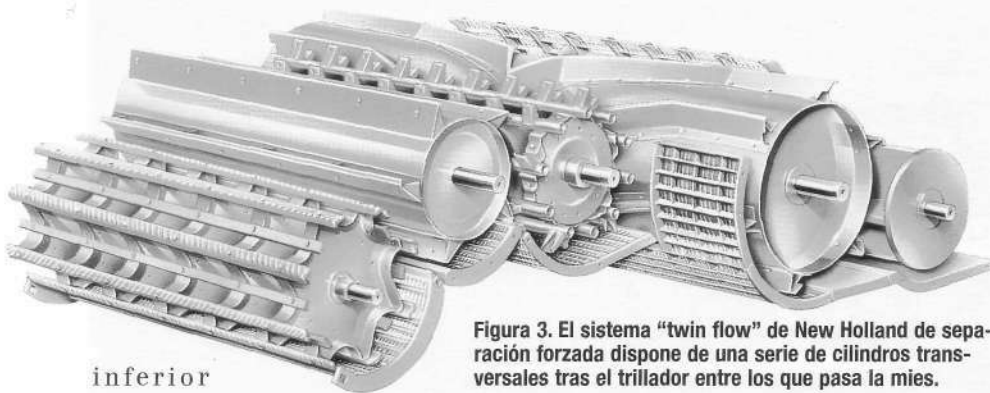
El sistema "twin flow" de New Holland de separación forzada dispone de una serie de cilindros transversales tras el trillador entre los que pasa la mies.
